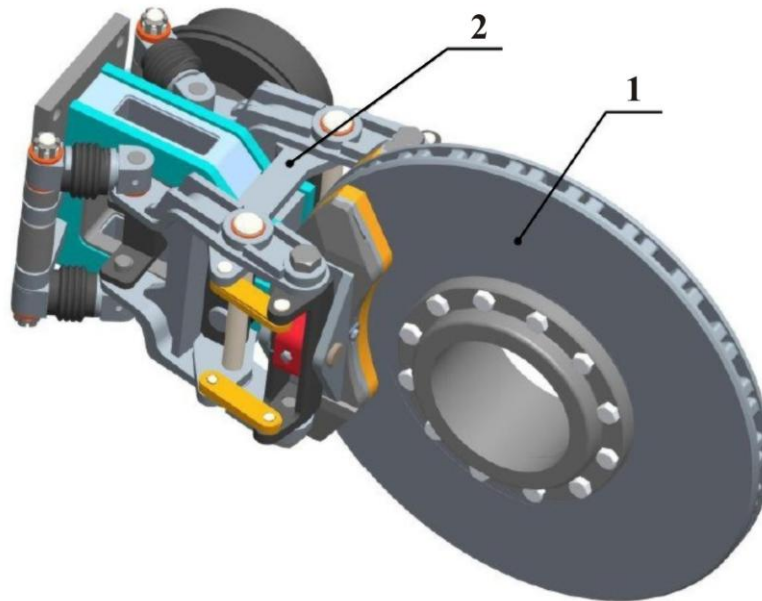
Важільний кліщовий механізм із пневматичним приводом дискового гальма: 1 - гальмовий диск; 2 - пневматичний привод.
